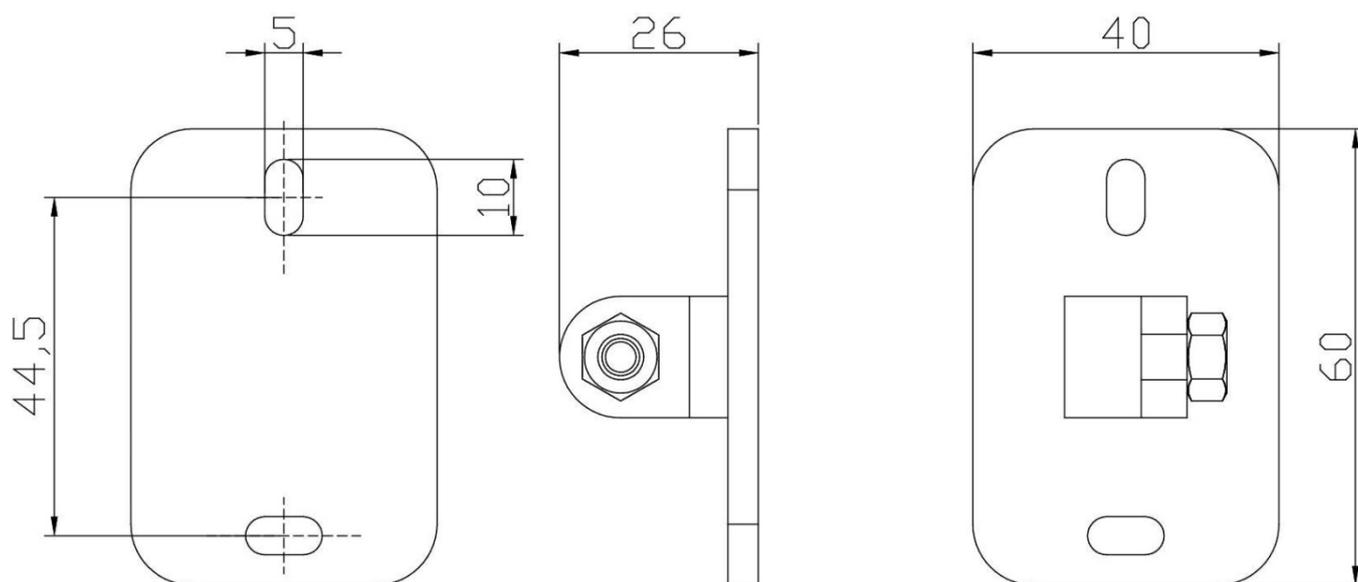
Габаритные и установочные размеры крепления извещателя «С2000-Спектрон-608».
